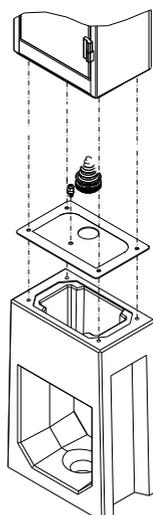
Vista esplosa della stazione di ricarica da montare su base
